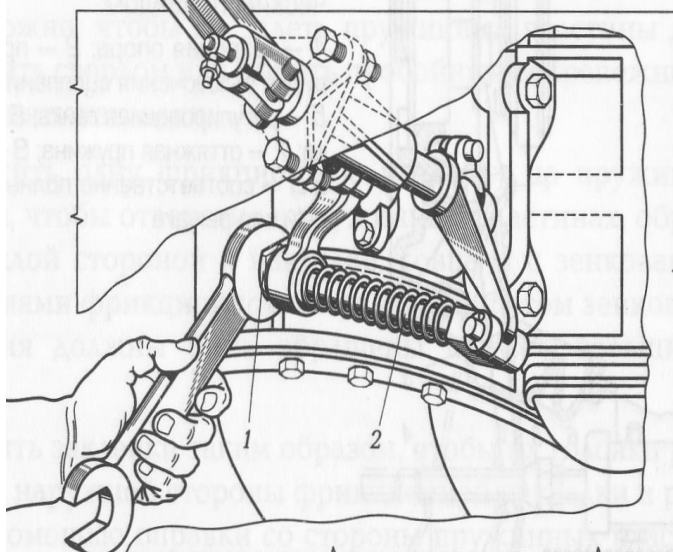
Регулировка свободного хода педали сцепления с механическим приводом: 1 — регулировочная гайка на тяге; 2 — тяга
